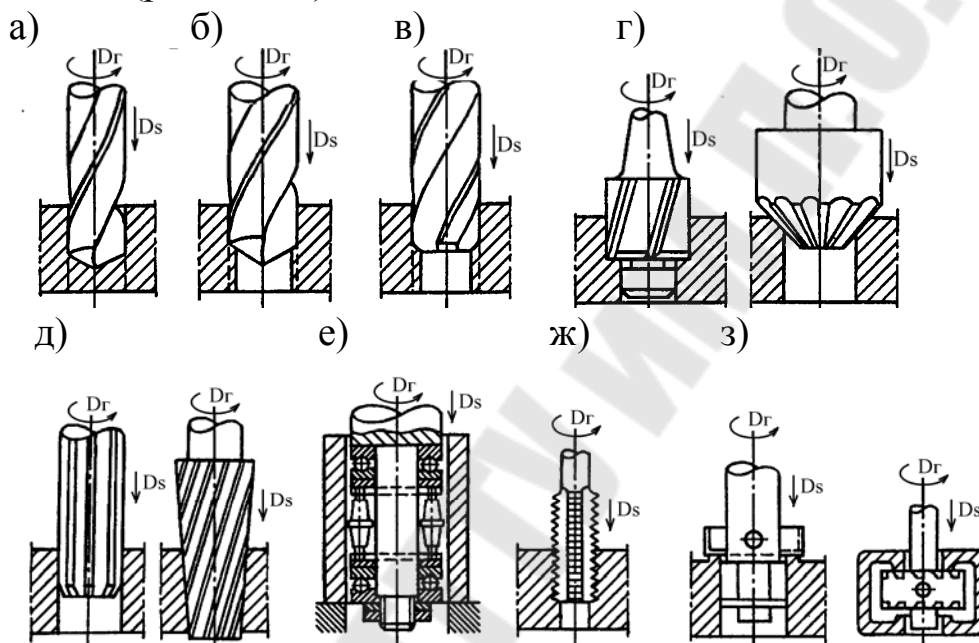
Работы, выполняемые на сверлильных станках: а – сверление; б – рассверливание; в – зенкерование; г – зенкование; д – развертывание; е – раскатывание; ж – нарезание внутренней резьбы; з – цекование (подрезание) торцов
